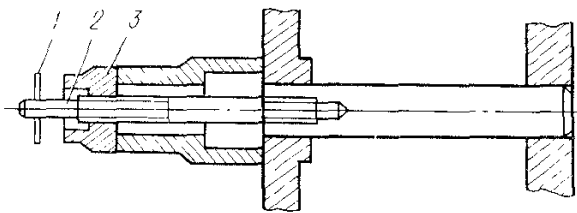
Съемник для выпрессовки оси блока шестерен заднего хода
